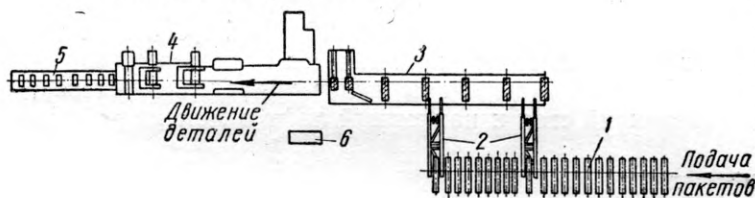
Схема автоматической подачи материала на четырехсторонний строгальный станок при помощи лифта:
